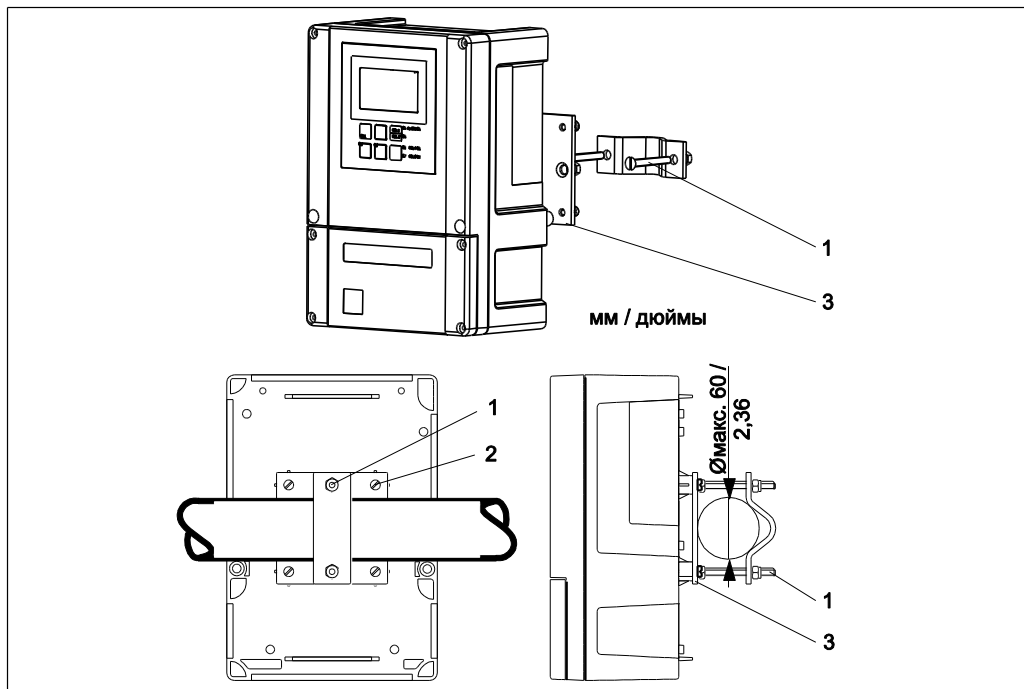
Монтаж полевого прибора на трубах цилиндрической формы
